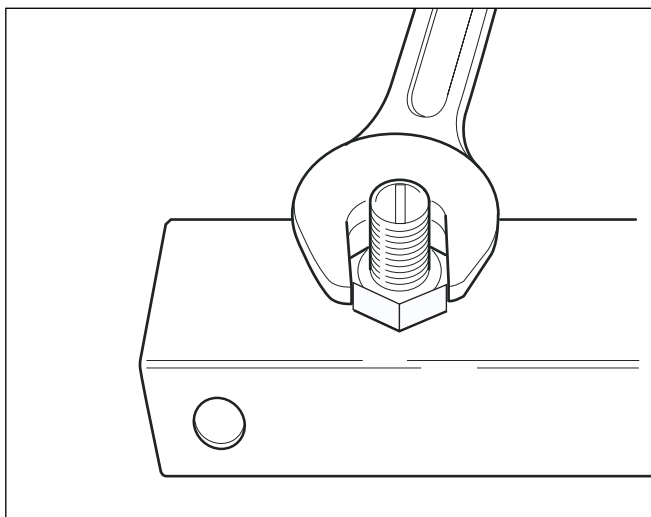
В двух угловых профилях (длиной 1014 мм) для держателя коллектора закрепить по два винта М 10х30. Гайки затянуть так, чтобы их боковые поверхности были перпендикулярны к продольным осям шин.
